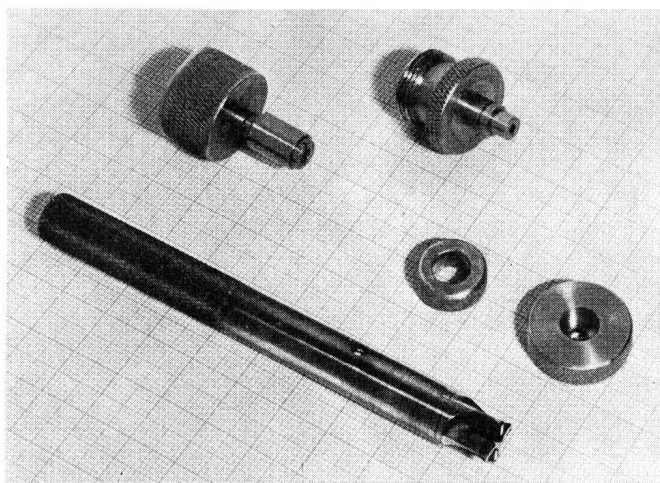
Montagewerkzeug für Stecker Typ A, B und F
